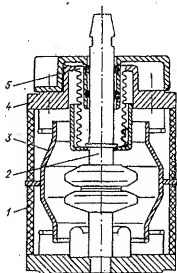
Конструкция и внешний вид вакуумной дугогасительной камеры:
